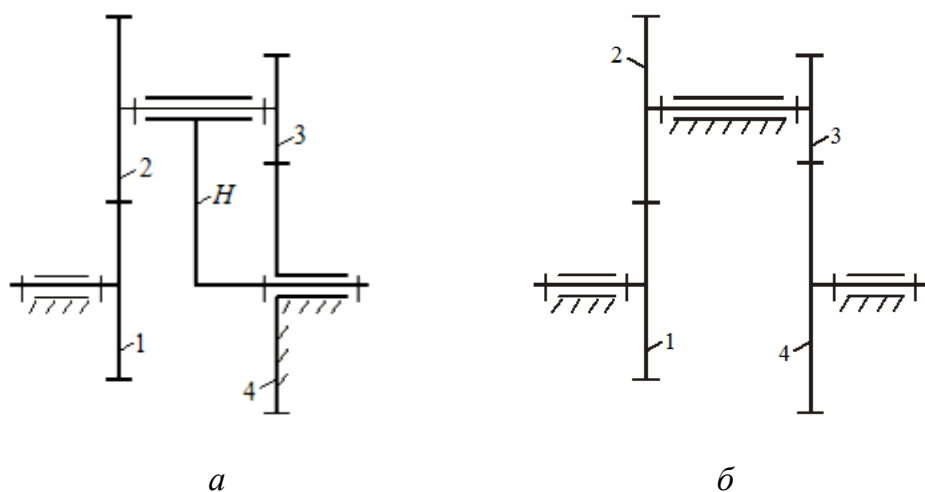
Метод обращенного движения: а – исходный планетарный механизм (редуктор Давида); б – соответствующий ему рядовой обращенный механизм
